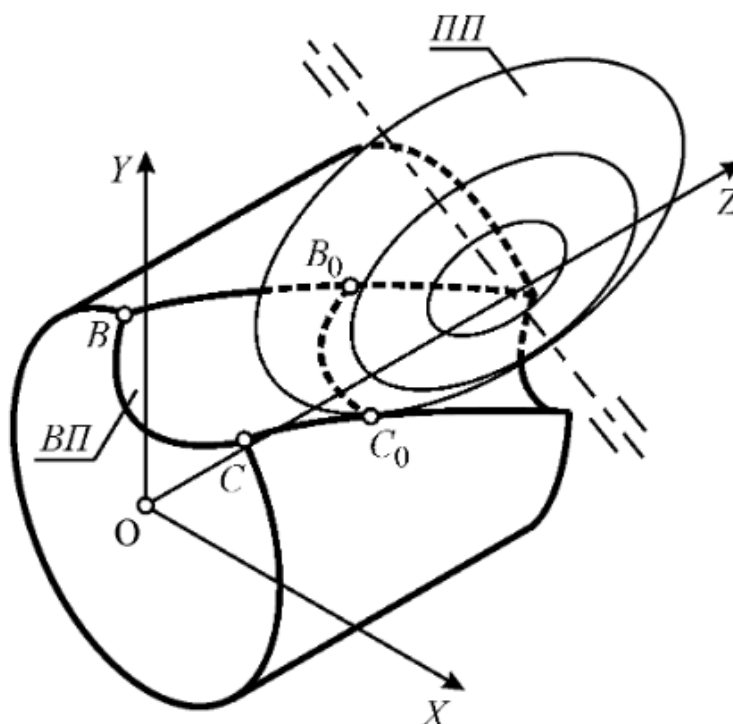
Касание ПП инструмента с ВП детали
